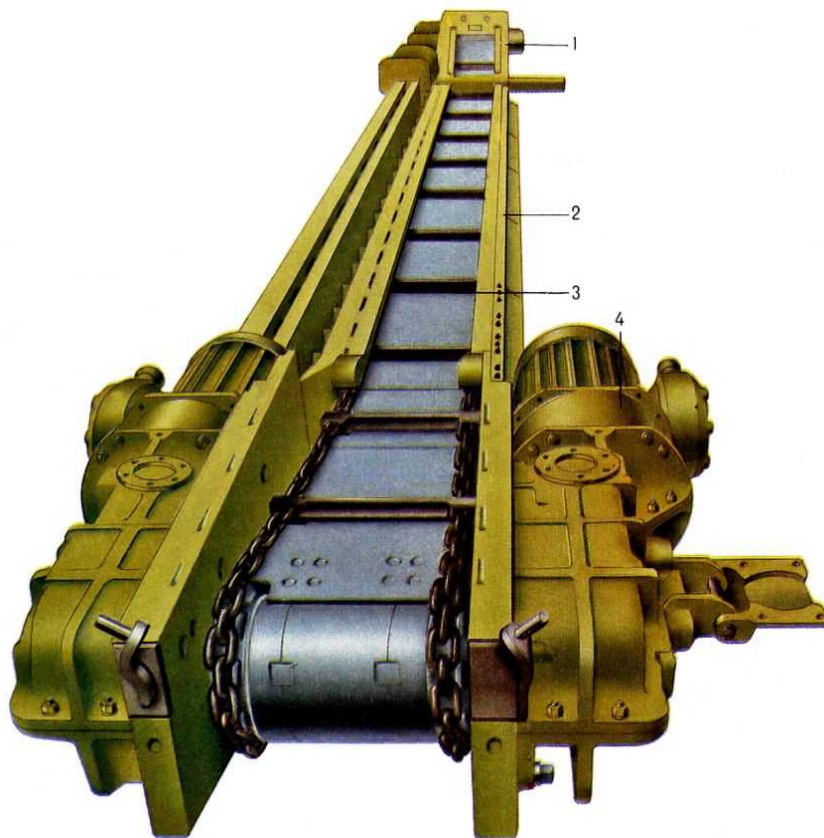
Скребковий конвеєр СП:1- натяжний пристрій; 2- рештчастий став; 3- тяговий ланцюг зі скребками; 4- приводний орган
